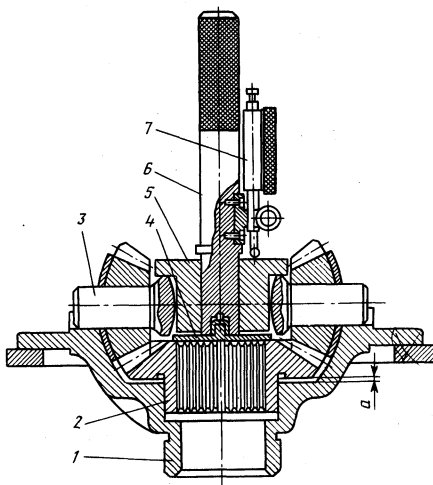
Приспособление для подбора упорных шайб дифференциала:
